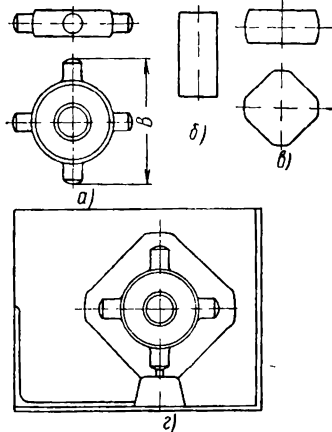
Схема штамповки крестовины из осажженной заготовки в одном окончательном ручье: а — поковка; б — исходная заготовка; в — заготовка после осадки; г — схема штампа
